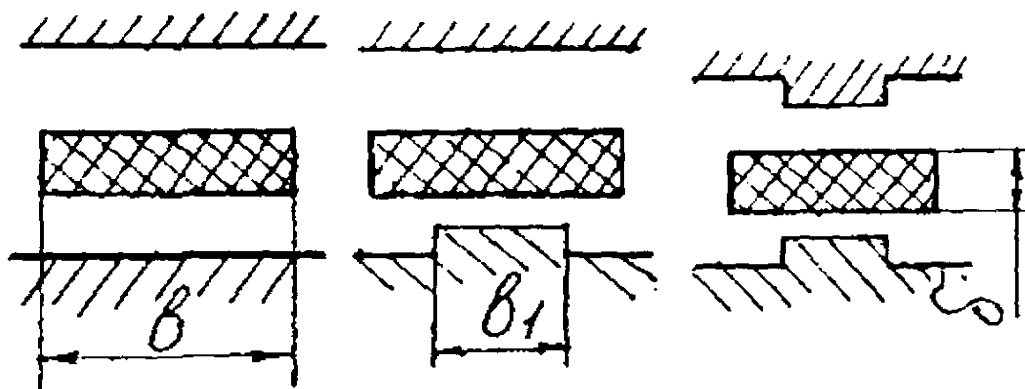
Схема размещения кольцевых прокладок между привалочными поверхностями:
